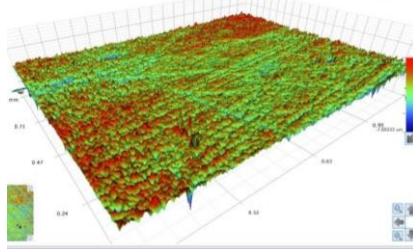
3D-модели поверхностной шероховатости на участках образца
